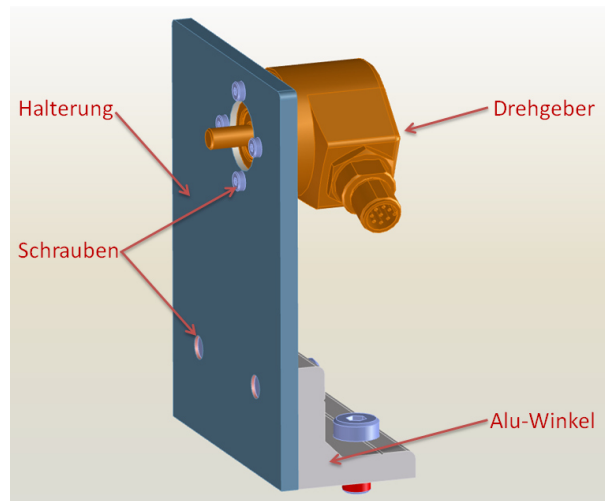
Prüfstand PV1710 CAD-Modell (Detailansicht: Aufnahme des Drehgebers)
